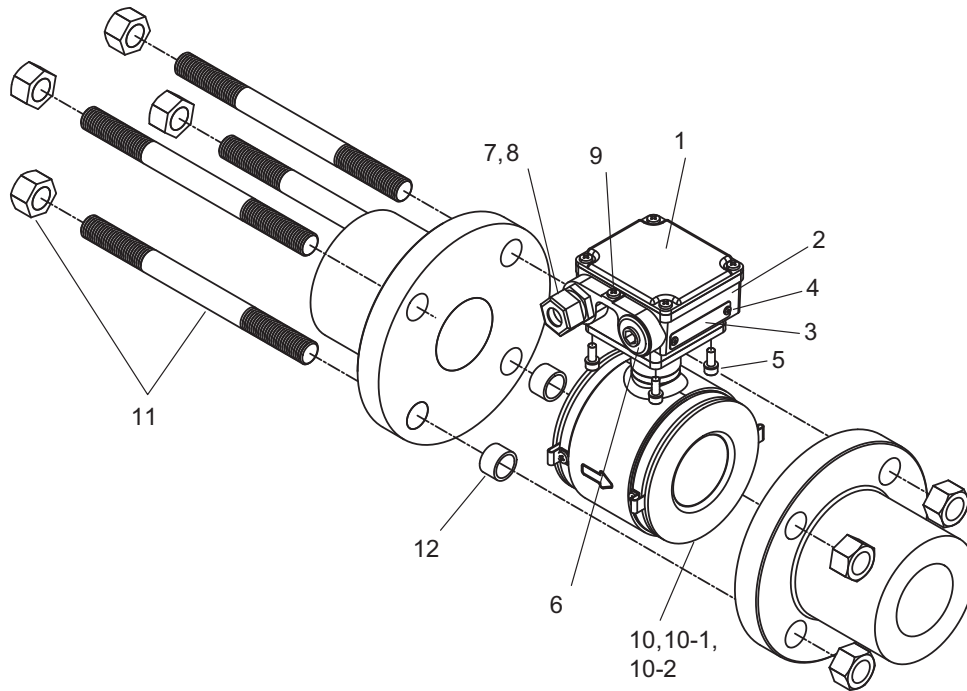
Pièces de rechange pour tube de mesure de type distant
